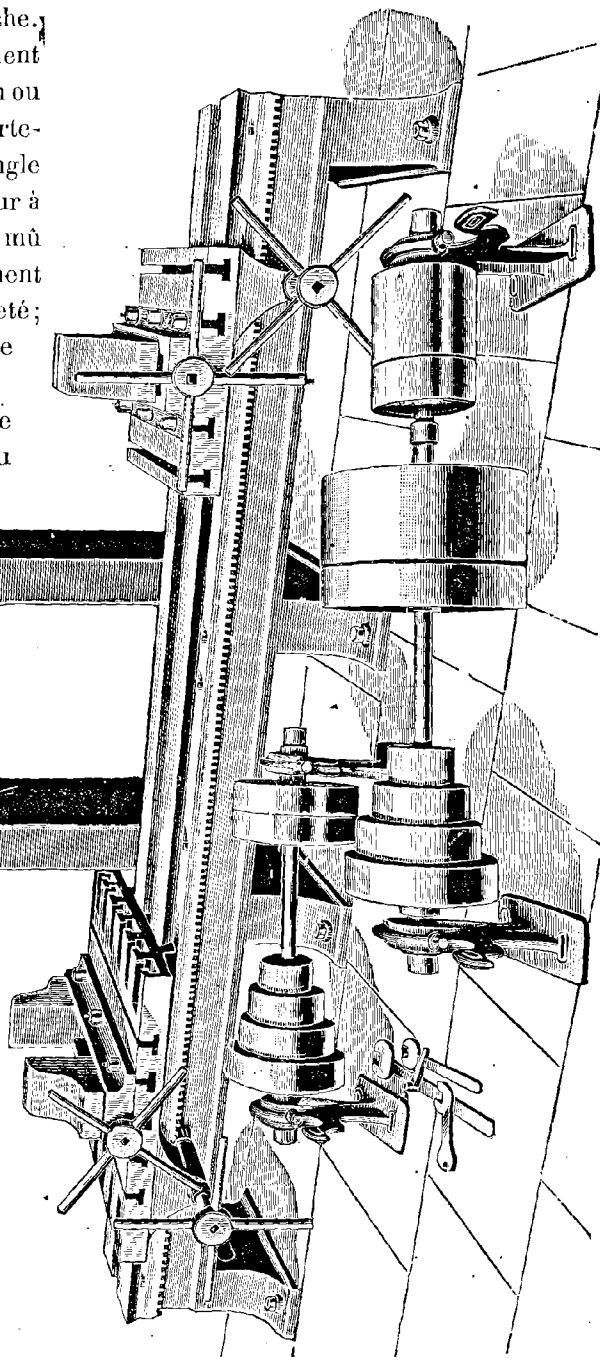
Machine double à percer et à tarauder de M. Lucas.
